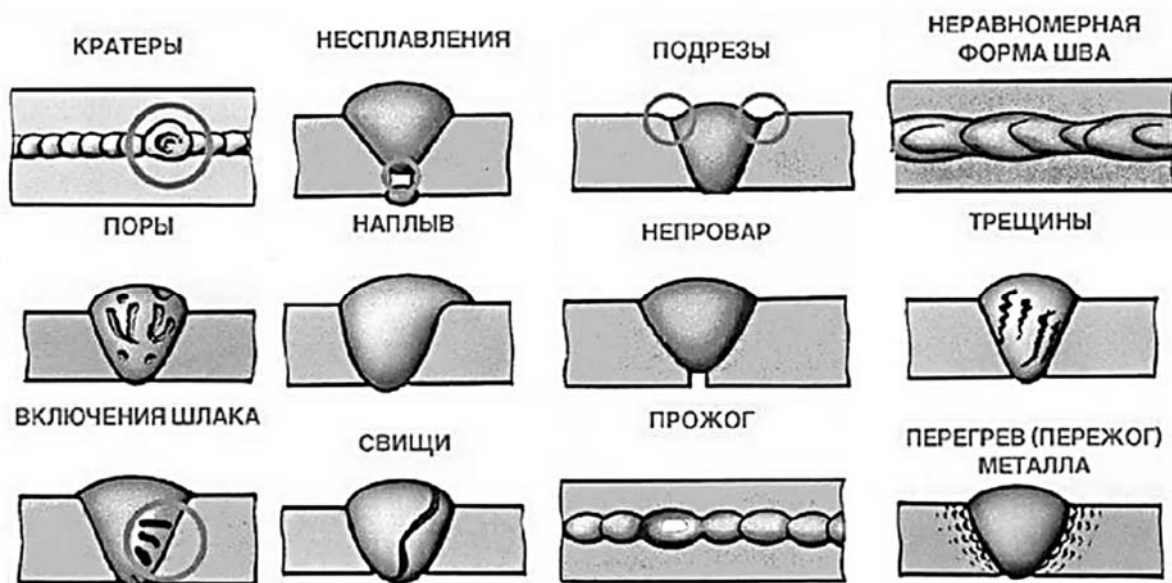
Дефекты формы и размеров сварных швов
